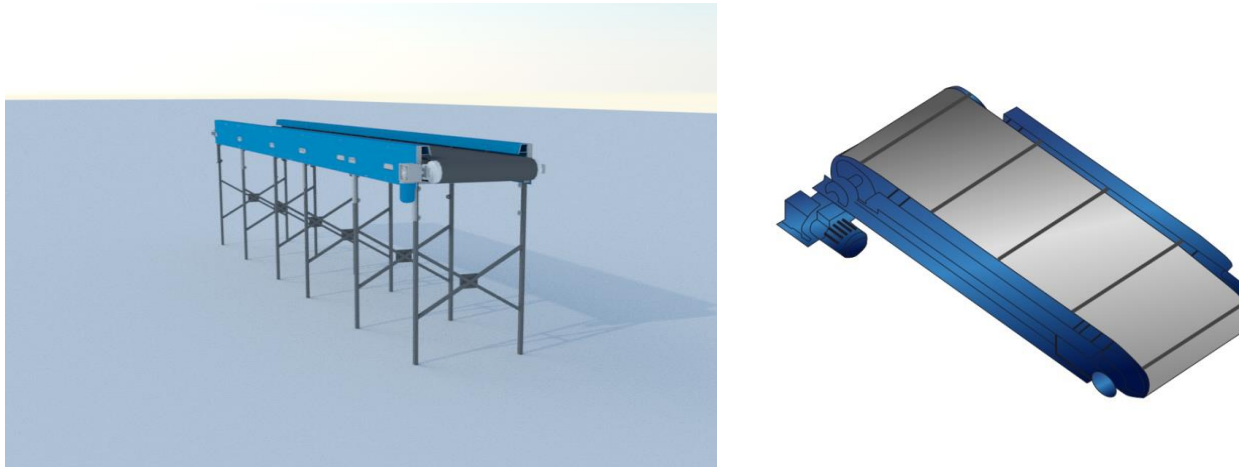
Ленточный конвейер основной сортировки и магнитный сепаратор
